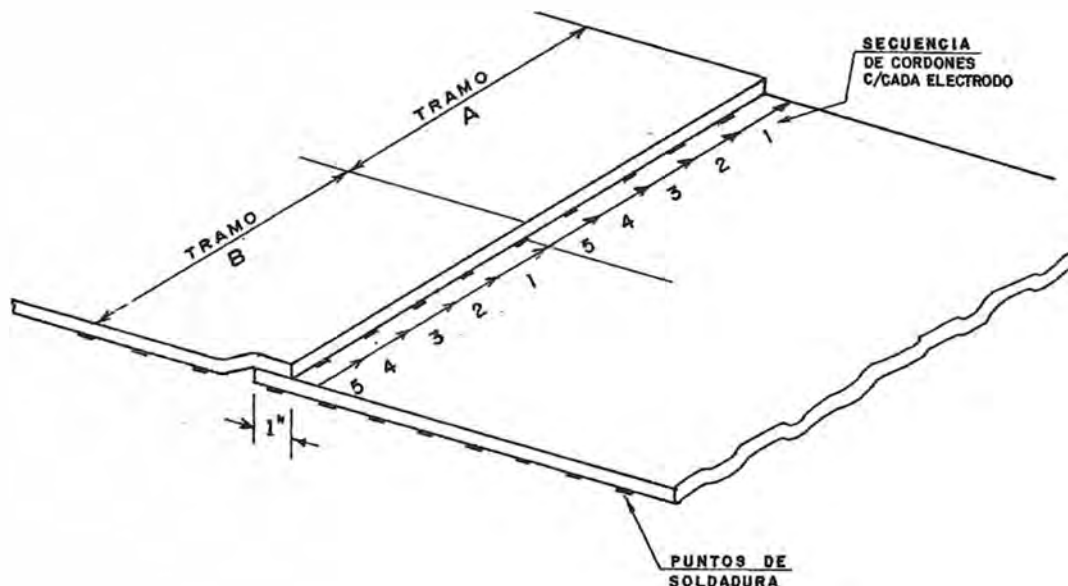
Método de soldadura "paso peregrino".
